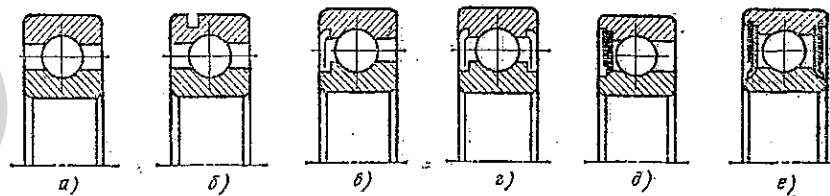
Шарикоподшипники радиальные однорядные типов: а — 00000; б — 50000; в — 60000; г — 80000; д — 160000; е — 180000
